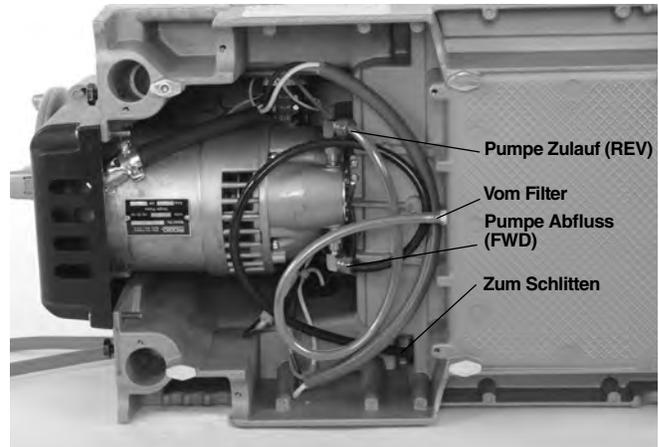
A – Ölpumpenanschlüsse für das Schneiden von Linksgewinden (Schalter auf REV)
